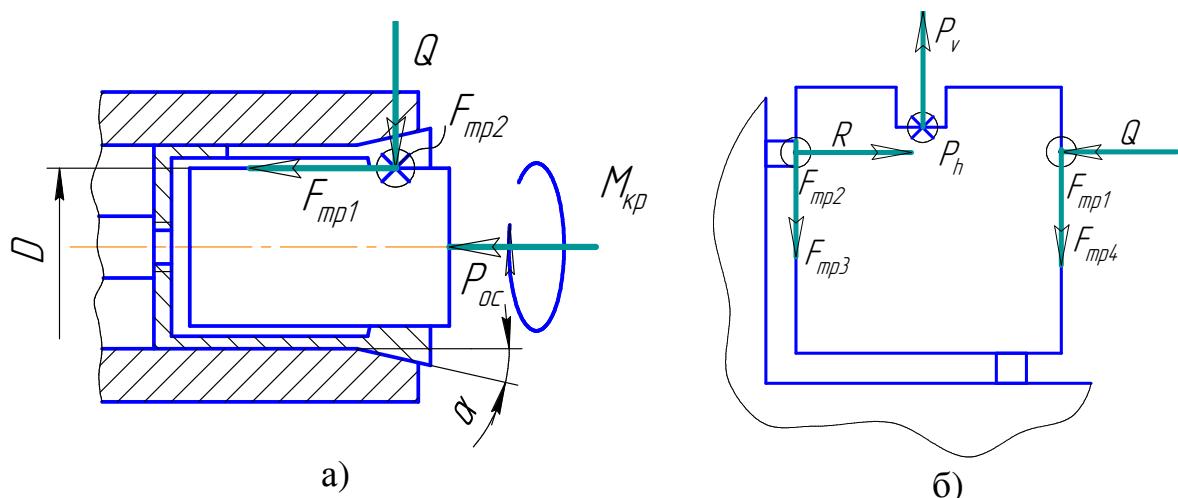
Расчетные схемы для определения усилий закрепления (а – при сверлении отверстия в заготовке, установленной в цанговом патроне; б - при фрезеровании паза)
